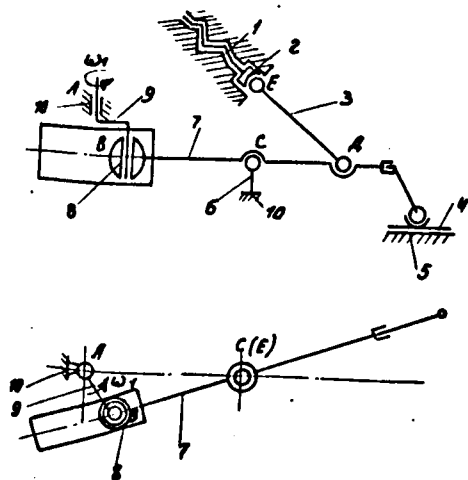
Кинематическая схема исключения опрокидывающего момента рычага:
